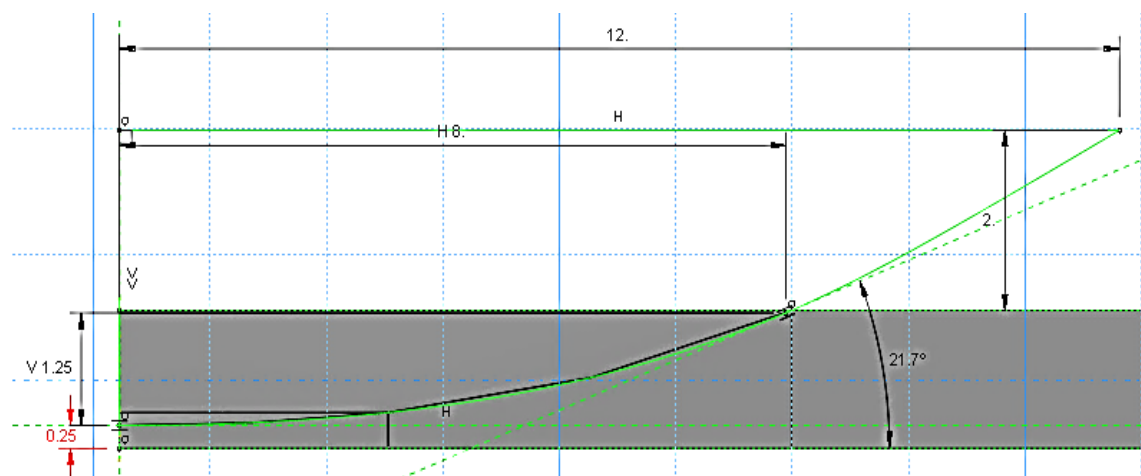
Espessura na zona crítica do modelo vista do plano (x,z)
